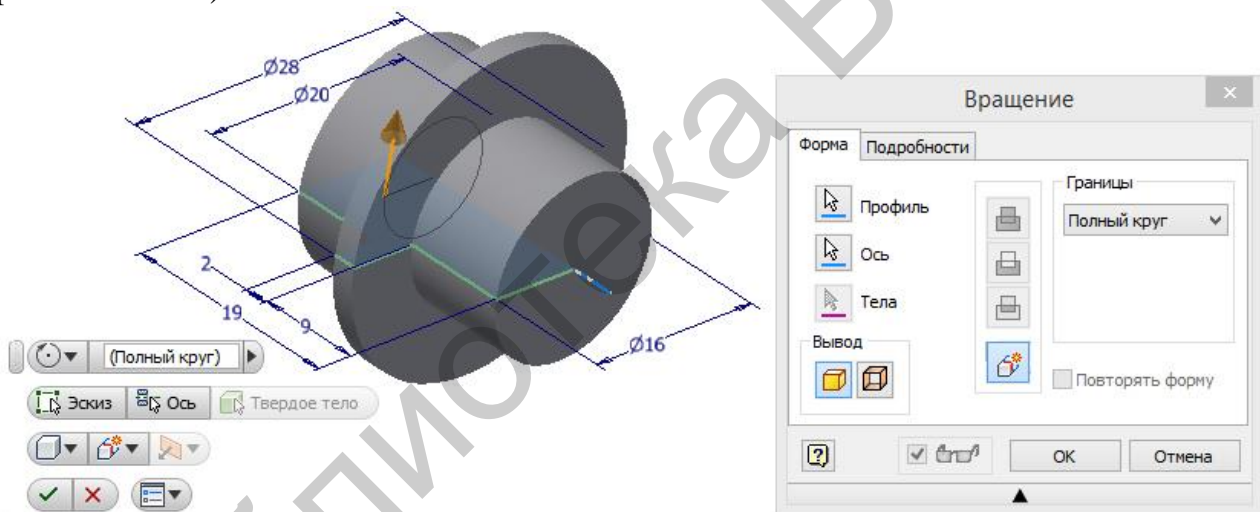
Построение цилиндрических частей заготовки детали «Крышка»
